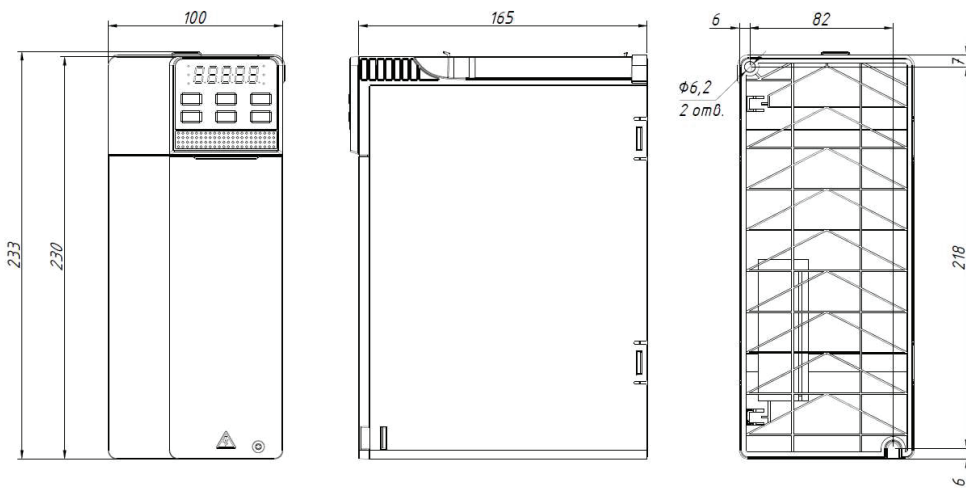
Чертеж преобразователя частоты типоразмера С3
